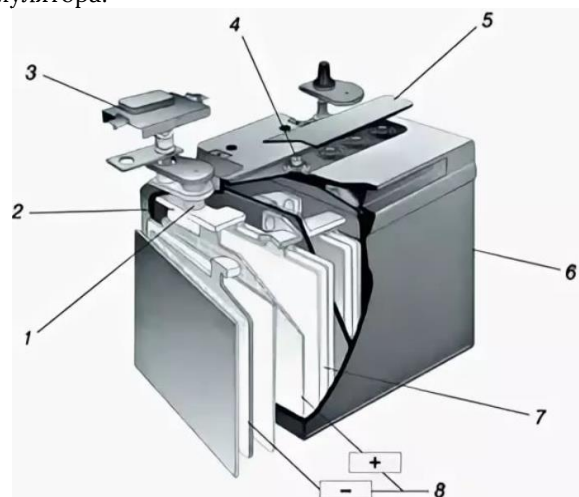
Схема устройства аккумуляторной батареи AGM типа: 1 – уплотнительное кольцо вывода; 2 – положительный вывод; 3 – изолирующая крышка; 4 – клапан избыточного давления; 5 – крышка клапанов; 6 – корпус; 7 – стекловолоконный сепаратор; 8 – положительные и отрицательные пластины.
